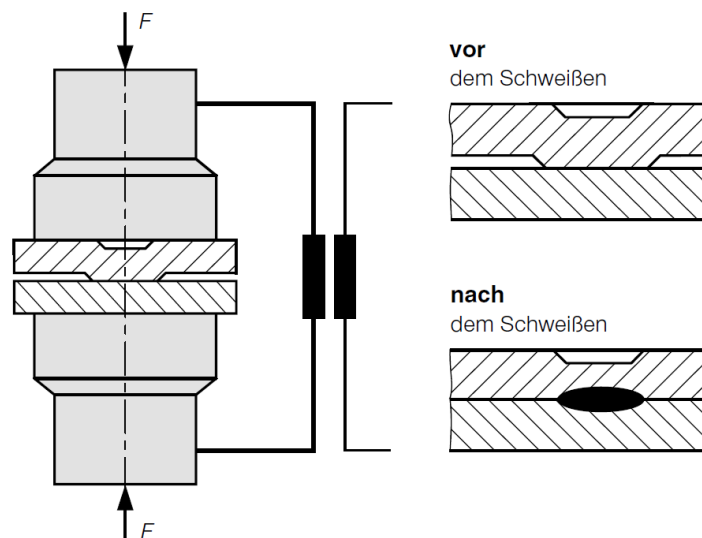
Verfahrensprinzip Buckelschweißen [5]
